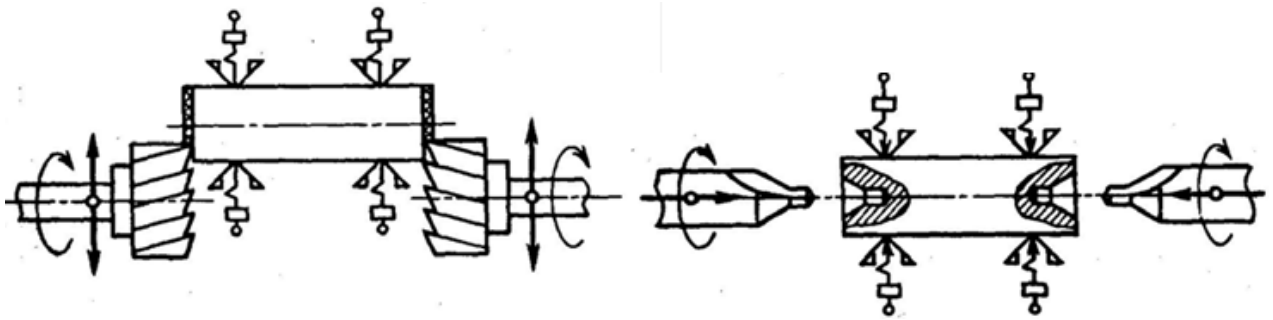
Схема роботи фрезерно-центрувального верстата
